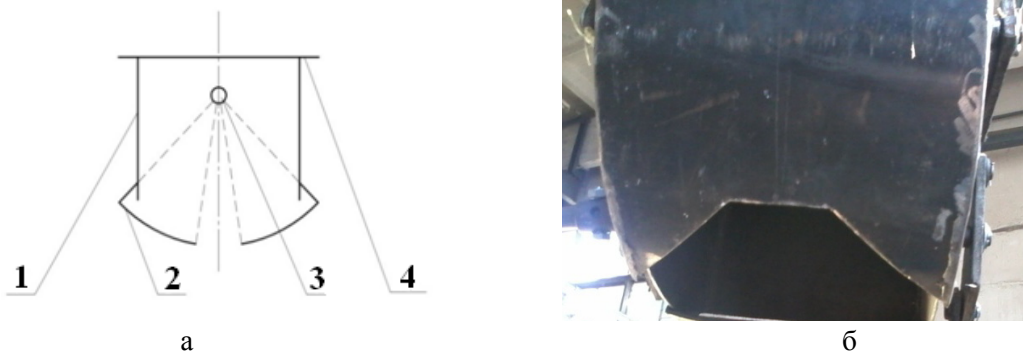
Принципиальная схема нового дозирующе-питающего устройства (а) и общий вид выпускной щели (б): 1 – корпус дозирующе-питающего устройства; 2 – ковш; 3– механизм регулирования раскрытия ковшей; 4 – соединительный фланец
